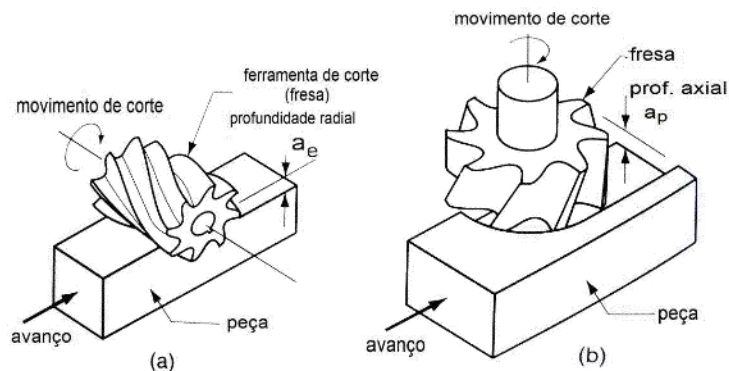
Processos de Fresagem: a) Fresagem cilíndrica; b) Fresagem frontal ou de topo [45].
